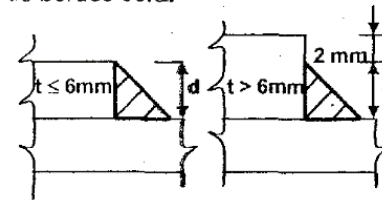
Tamaño máximo de soldaduras de filete (bibliografía 22)
